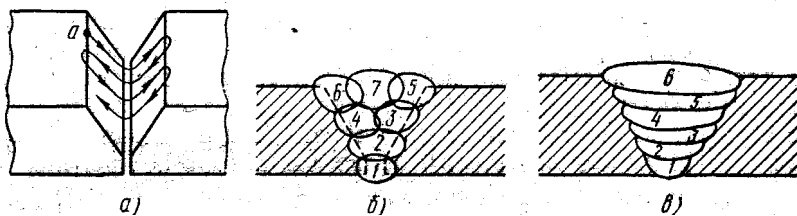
Сварка стыковых швов (цифрами обозначен порядок наложения слоев шва):
